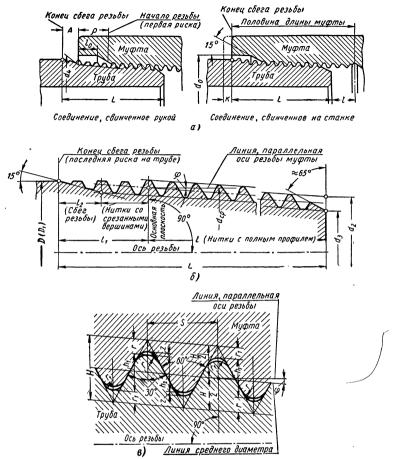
Трубные конические резьбы нефтепромышленности: a — схема соединения; b — длины свинчивания и другие элементы; b — профильрезьбы
